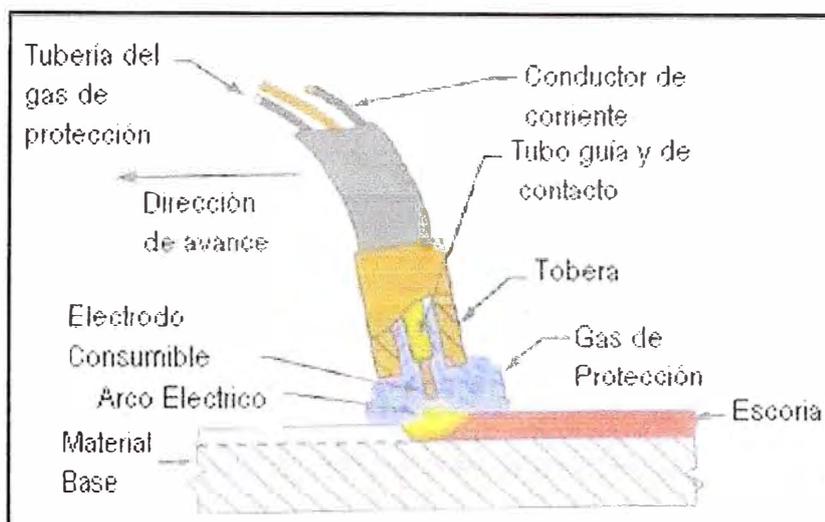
Proceso de Soldadura GMAW
